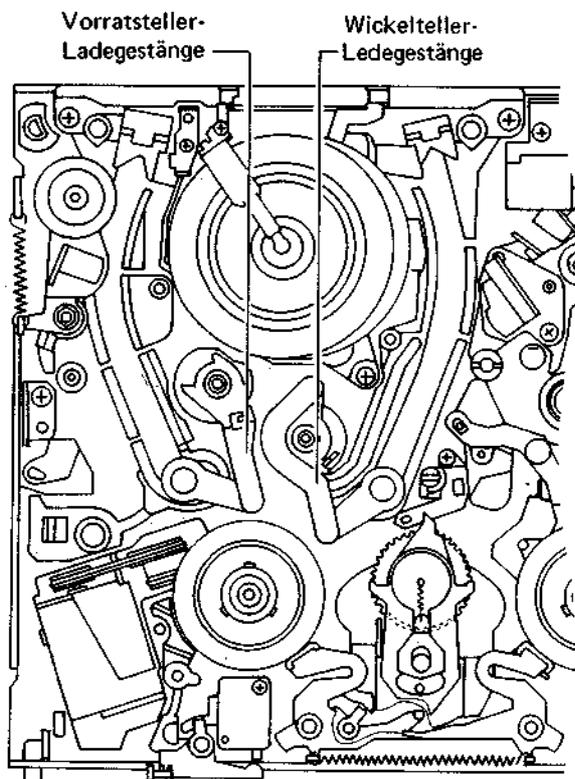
Draufsicht auf das Bandlaufwerk (bei ausgebautem Hilfschassis)
